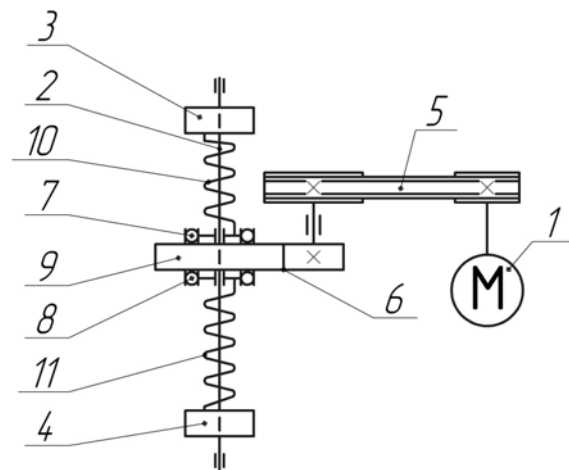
Кінематична схема привода круглов'язальної машини: 1 – електродвигун; 2 – вертикальний приводний вал; 3, 4 – шестерні; 5 – клинопасова передача; 6 – зубчаста передача; 7, 8 – обгінні муфти; 9 – зубчасте колесо; 10, 11 – пружини кручення
